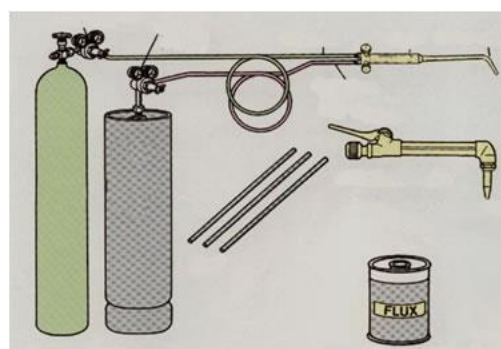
Equipo Utilizado para la Soldadura Fuerte
